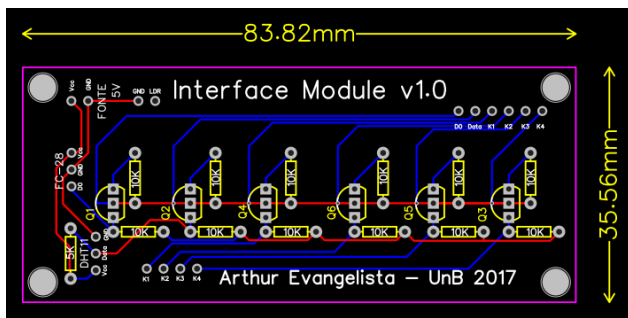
Layout para PCB a ser confeccionada para o projeto.
